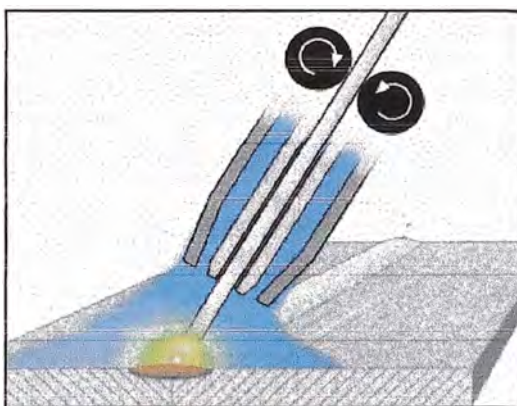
Esquema del proceso de soldadura GMAW.
